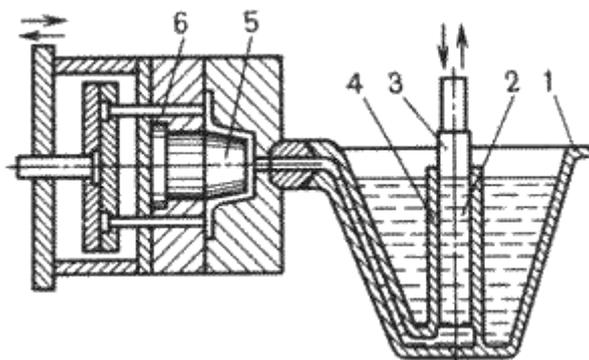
Схема изготовления отливки на машинах с горячей камерой прессования
